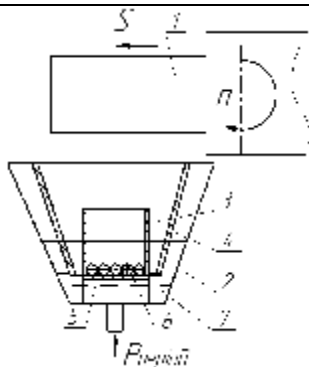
Схема вібраційного гідравлічного кулькоударного обладнання: 1 – деталь; 2 – ванна; 3 – сопло; 4 – прийомна сітка; 5 – кульки; 6 – розподільча сітка; 7 – рідина
